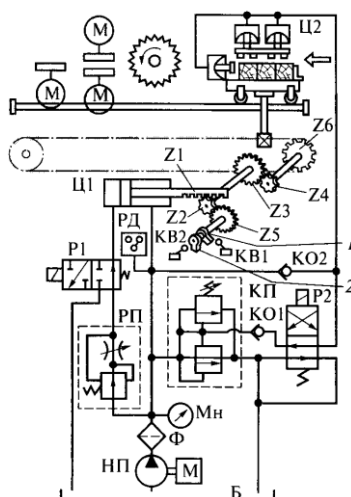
Гідрокінематична схема одnobічного рамного шипорізного верстата: 1, 2 – кулачки
